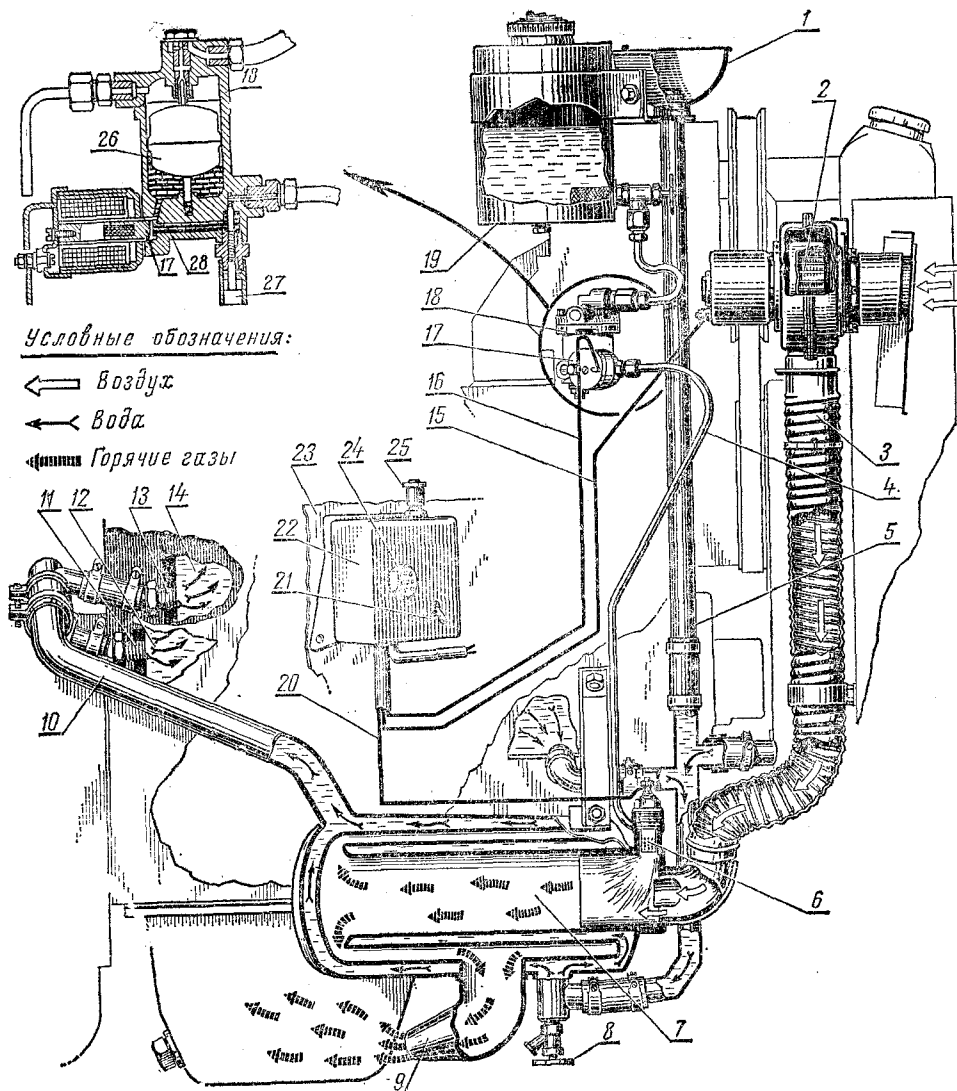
Подогреватель охлаждающей жидкости двигателя ЗИЛ-130:
